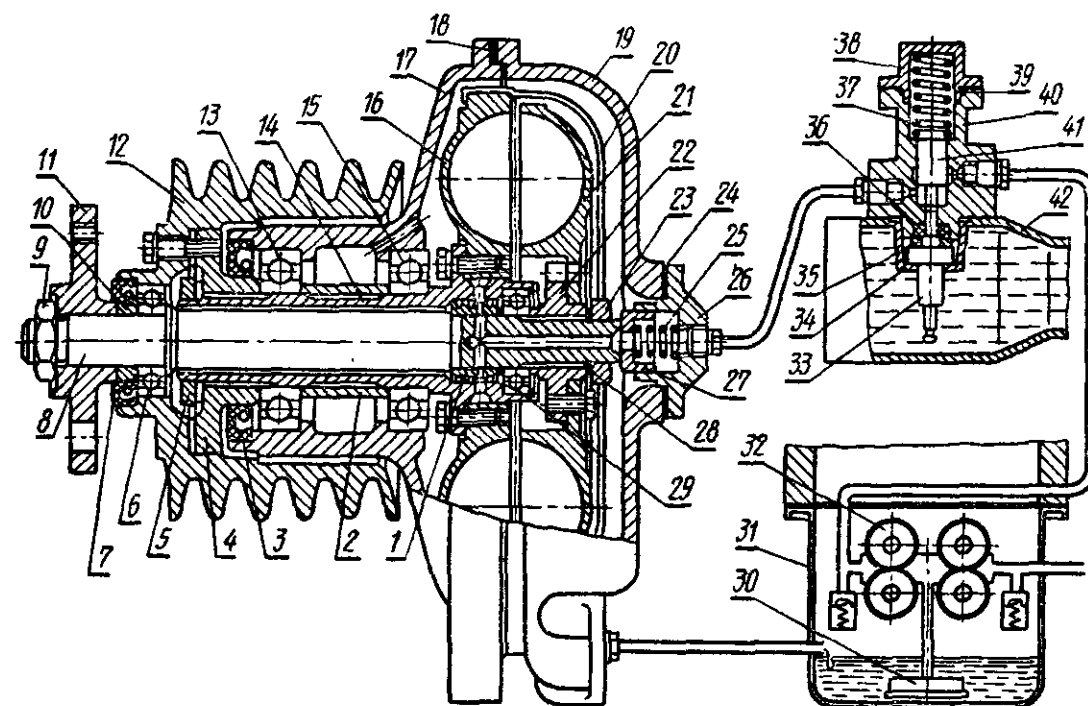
Гидросистема автоматического управления вентилятором: 1, 2, 10 и 27 — втулки; 3 и 7 — манжеты; 4, 11 и 22 — ступицы; 5, 9, 23 и 34 — гайки; 6, 13, 15 и 29 — подшипники; 8 — ведомый вал; 12 — шкив; 14 — ведущий вал; 16 — ведущее колесо; 17 и 40 — корпуса; 18, 24 и 28 — прокладки; 19 — корпус-кронштейн; 20 — кожух; 21 — ведомое колесо; 25 и 37 — пружины; 26 — фланец; 30 — маслозаборник; 31 — поддон; 32 — масляный насос; 33 — датчик; 35 — регулировочная шайба; 36 и 39 — уплотнительные кольца; 38 — крышка; 41 — золотник; 42 — водяная труба.
